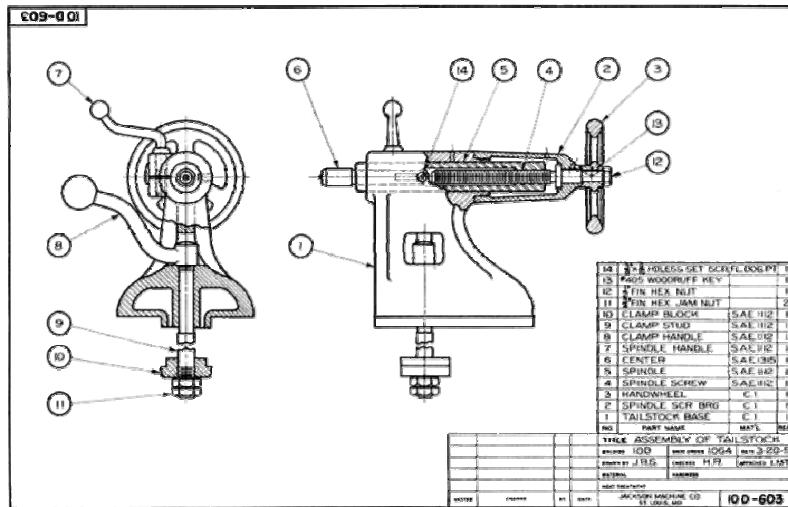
ภาพเขียนแบบการประกอบแบบ exploded assembly
